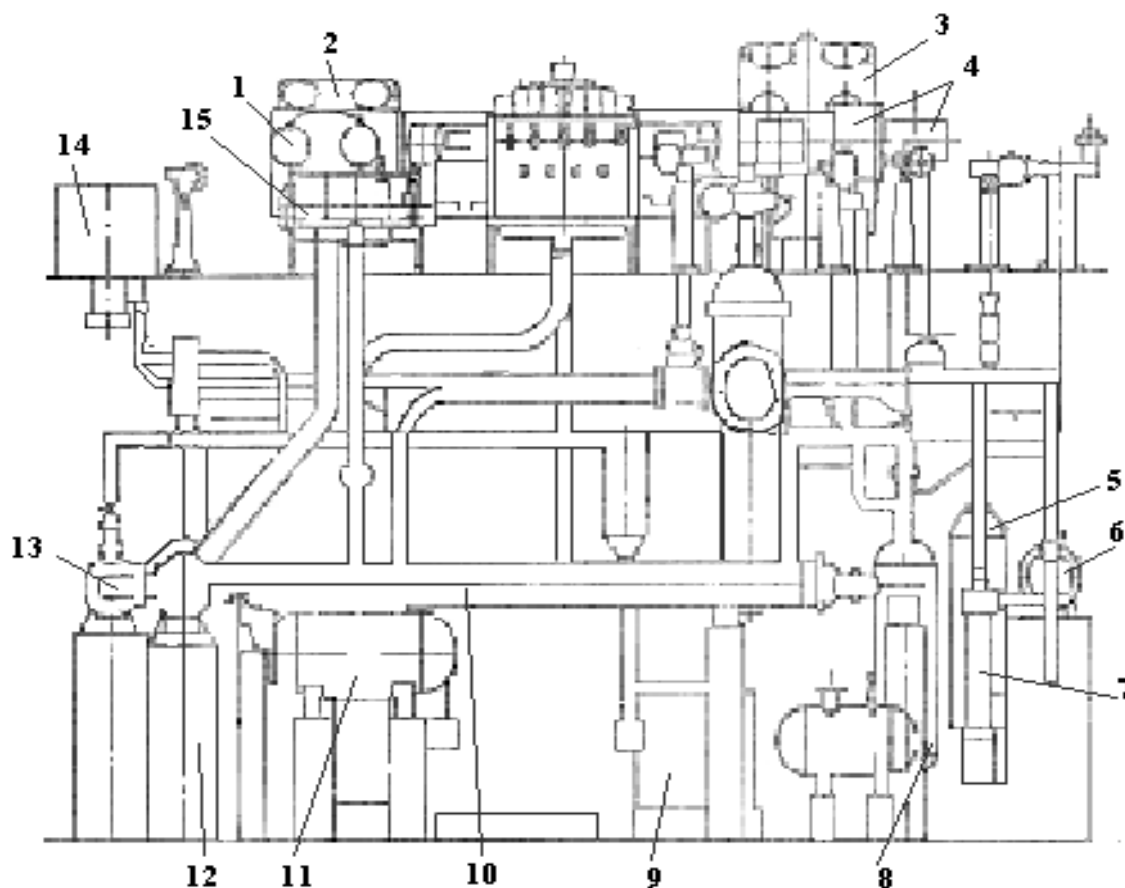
Схема поршневого компрессора 4М16-100/200
